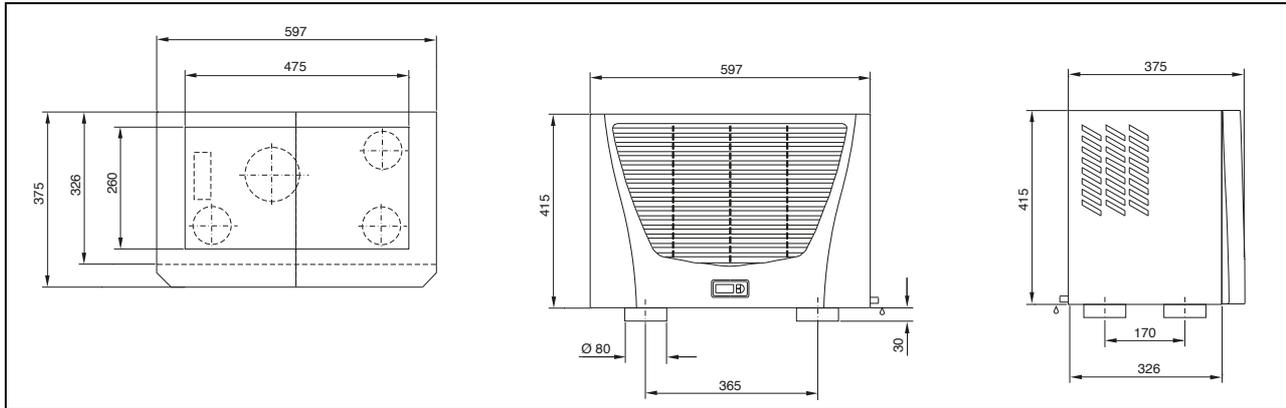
3359.xxx, 3382.xxx montaje interior
